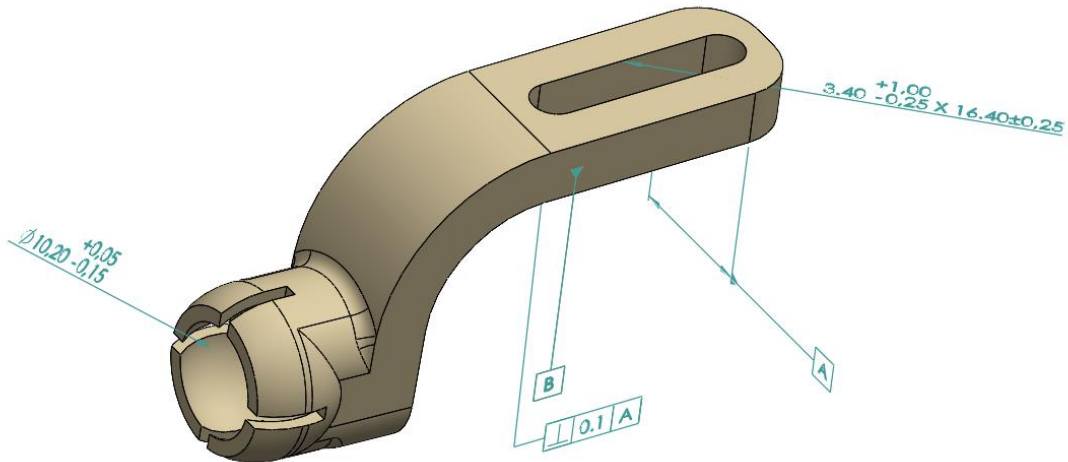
Tolerancias dimensionales “Extensión muñeca-pulgar”
